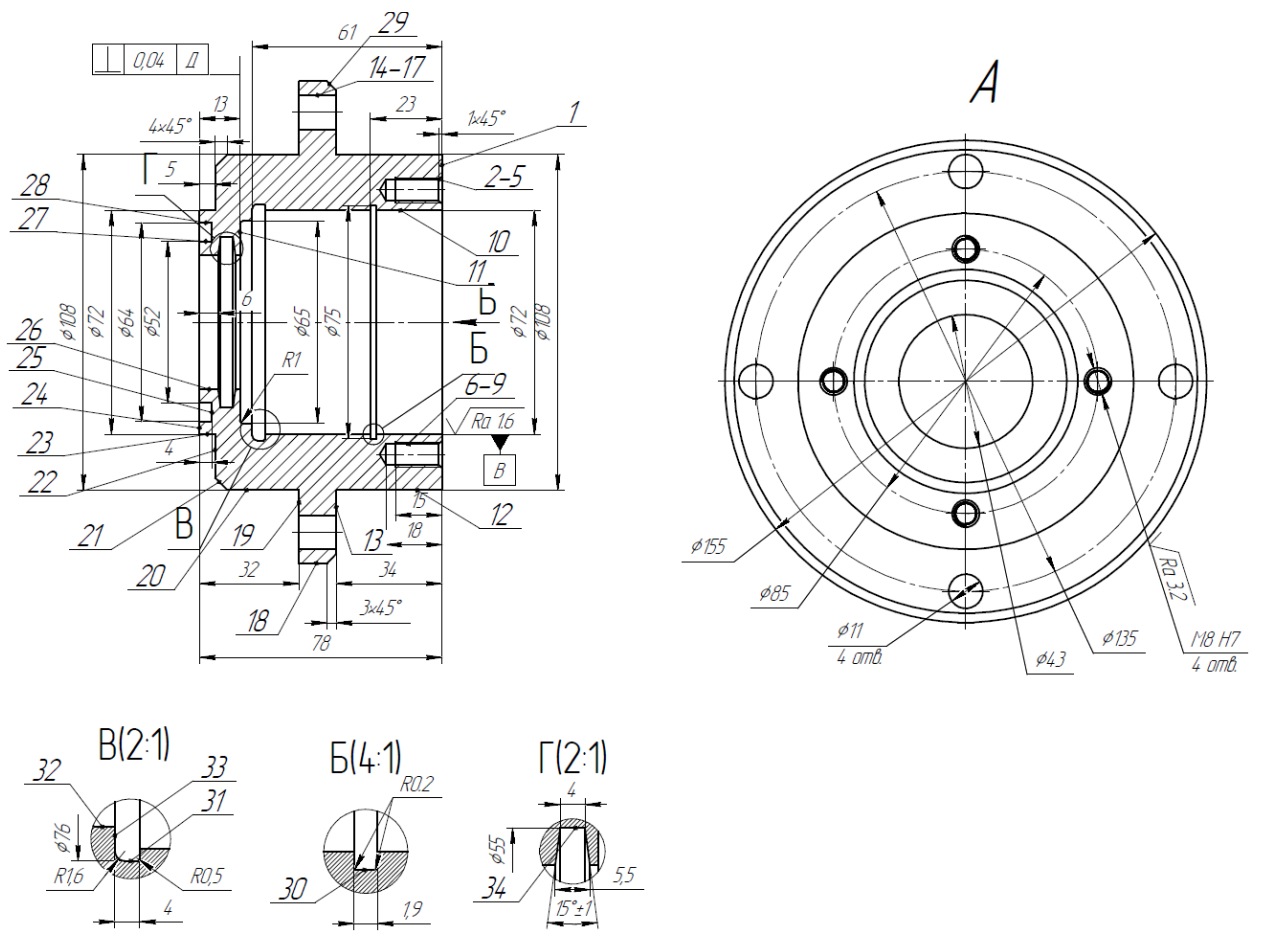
Ескіз деталі із номерами її поверхонь
